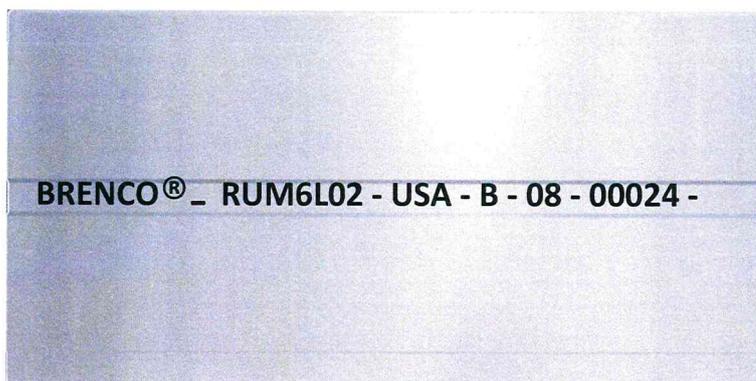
Маркировка наружного кольца кассетного подшипника торговой марки BRENCO (EPK- BRENCO).
